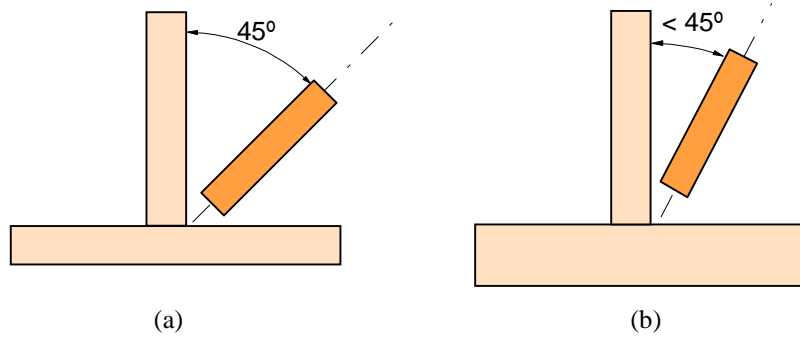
Posicionamento para a soldagem de juntas em T de (a) chapas da mesma espessura e (b) chapas de espessuras diferentes.
